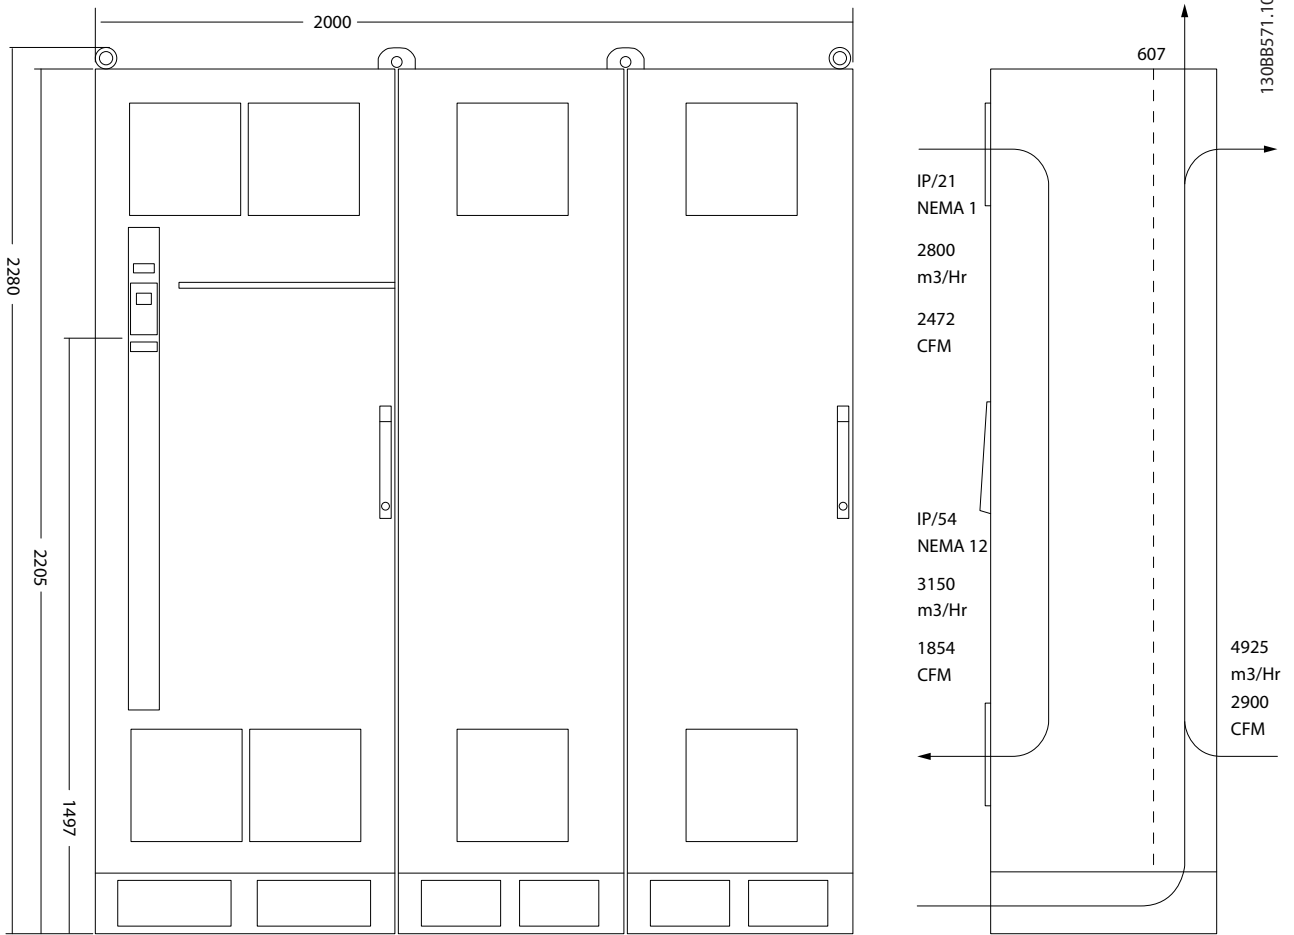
Mechanische afmetingen (mm), F10
